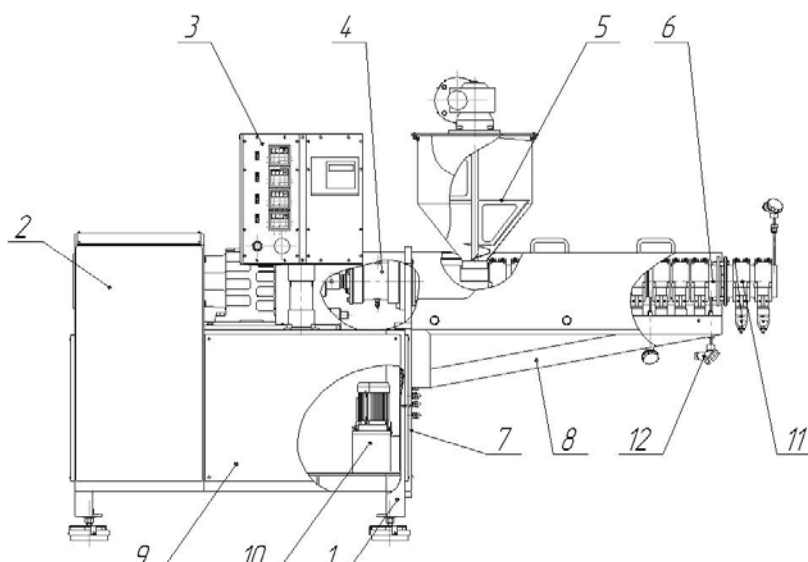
Внешний вид экструдера: 1 – станина; 2 – шкаф электрический; 3 – пульт управления; 4 – подшипниковый узел; 5 – ворошитель; 6 – корпус; 7 – поворотная плита; 8 – опора корпуса; 9 – жалюзи; 10 – станция смазки; 11 – нагреватель; 12 – термопара
